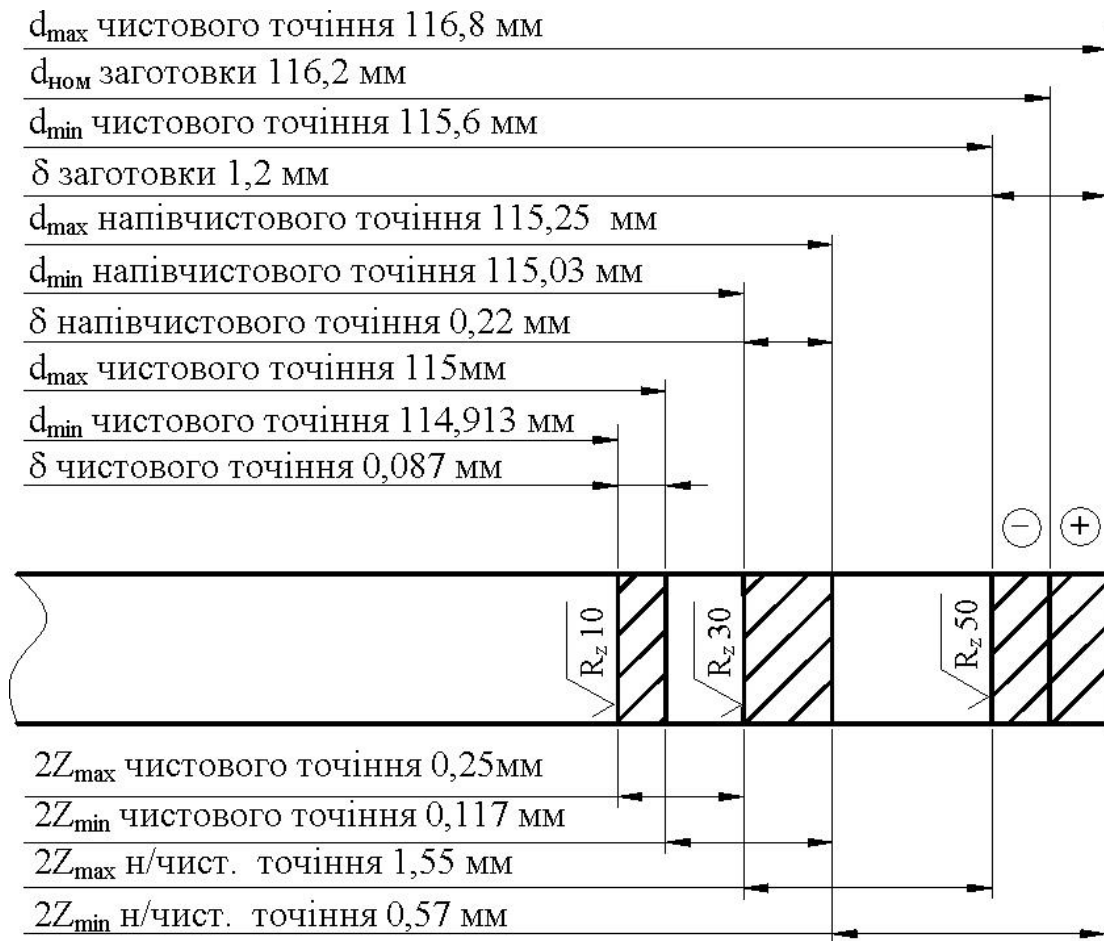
Схема припусків для обробки поверхні $\varnothing 115h9_{(-0,087)}$
